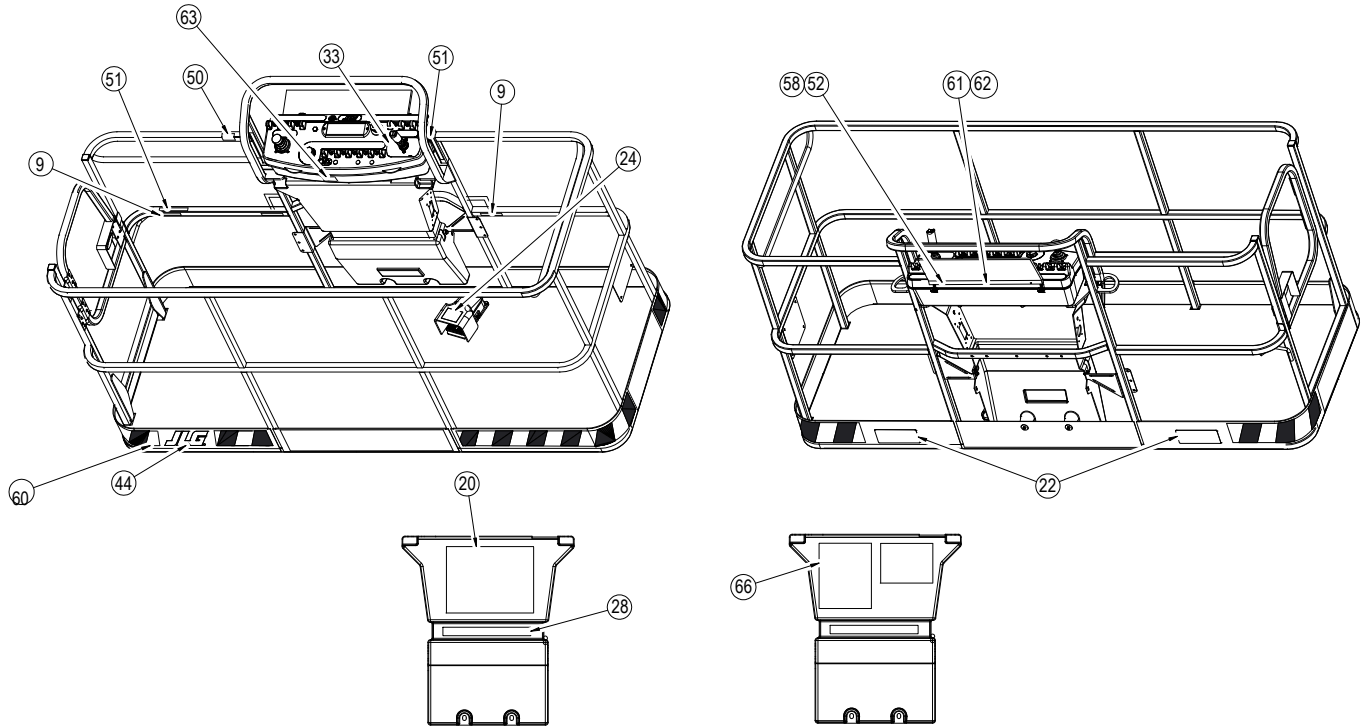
Dekalplacering - Serienummer 0300141446 till nu - Endast CE - Blad 3 av 5
